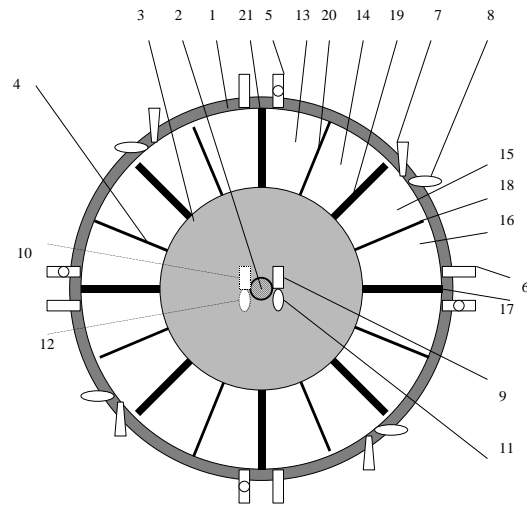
Двигатели в торе-двигателе внутреннего сгорания с двумя роторными лопастно-поршневыми крыльчатками
